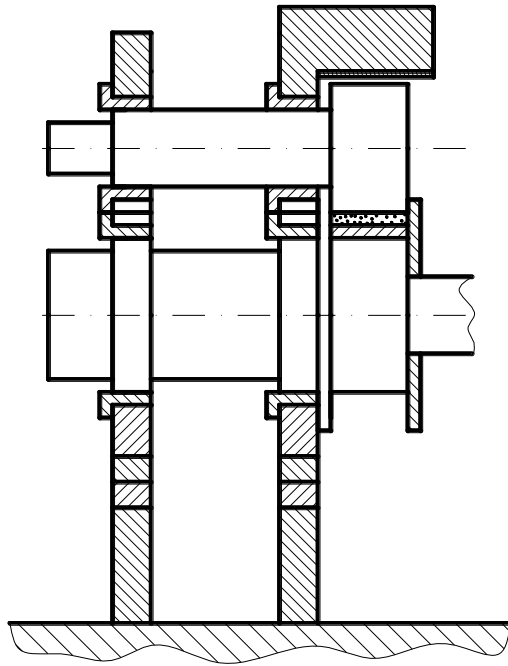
Стан для прокатки порошков с консольно расположенными валками
